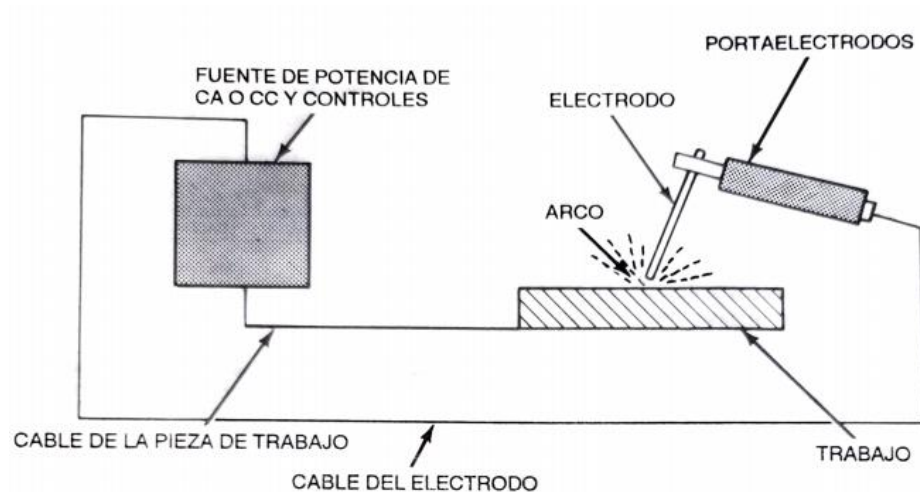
Elementos de un circuito de soldadura SMAW [1]
